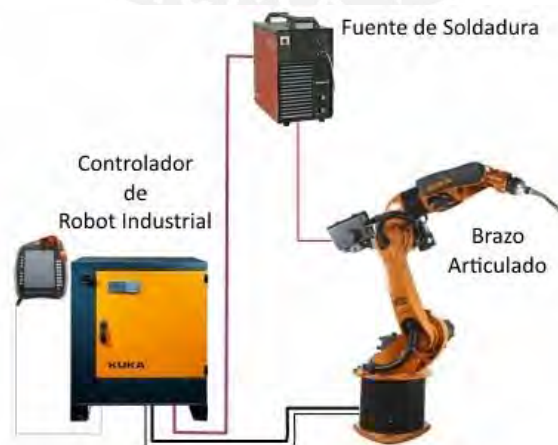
Integración de un robot industrial con fuente de soldadura, Fuente: KUKA.com
